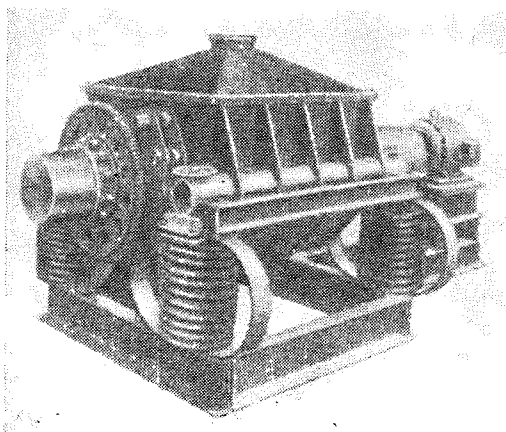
Крупная вибромельница для размола твердосплавных смесей
